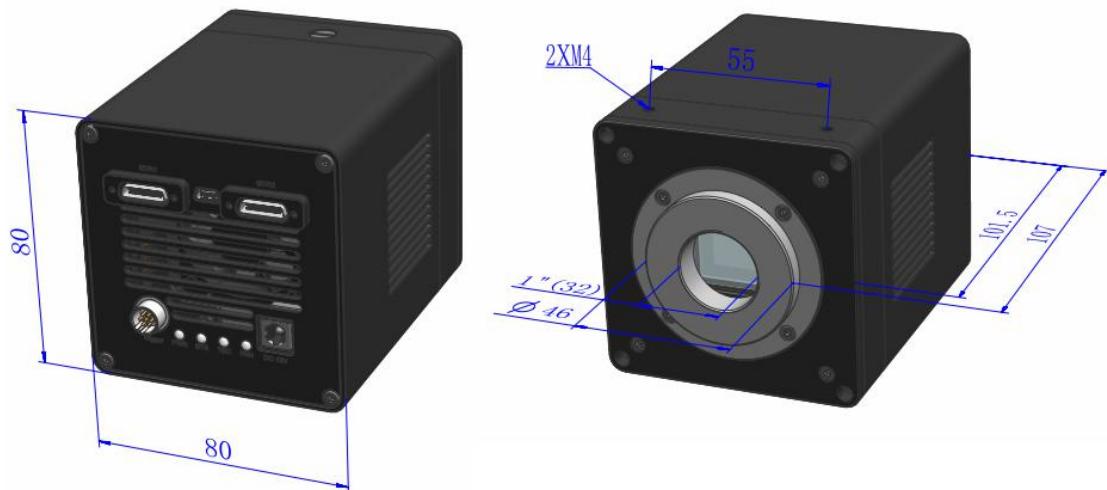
sMAX04BM-CL100 整机尺寸(单位: mm)
